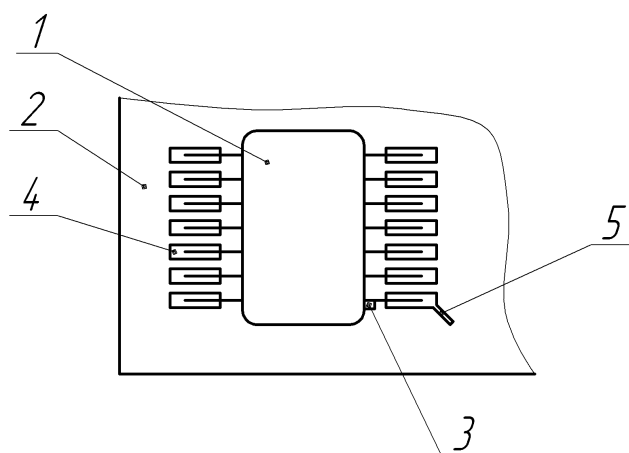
Расположение микросхем с планарными выводами на печатной плате: 1 – микросхема; 2 – плата печатная; 3 – первый вывод микросхемы; 4 – площадка контактная; 5 – ключ.
